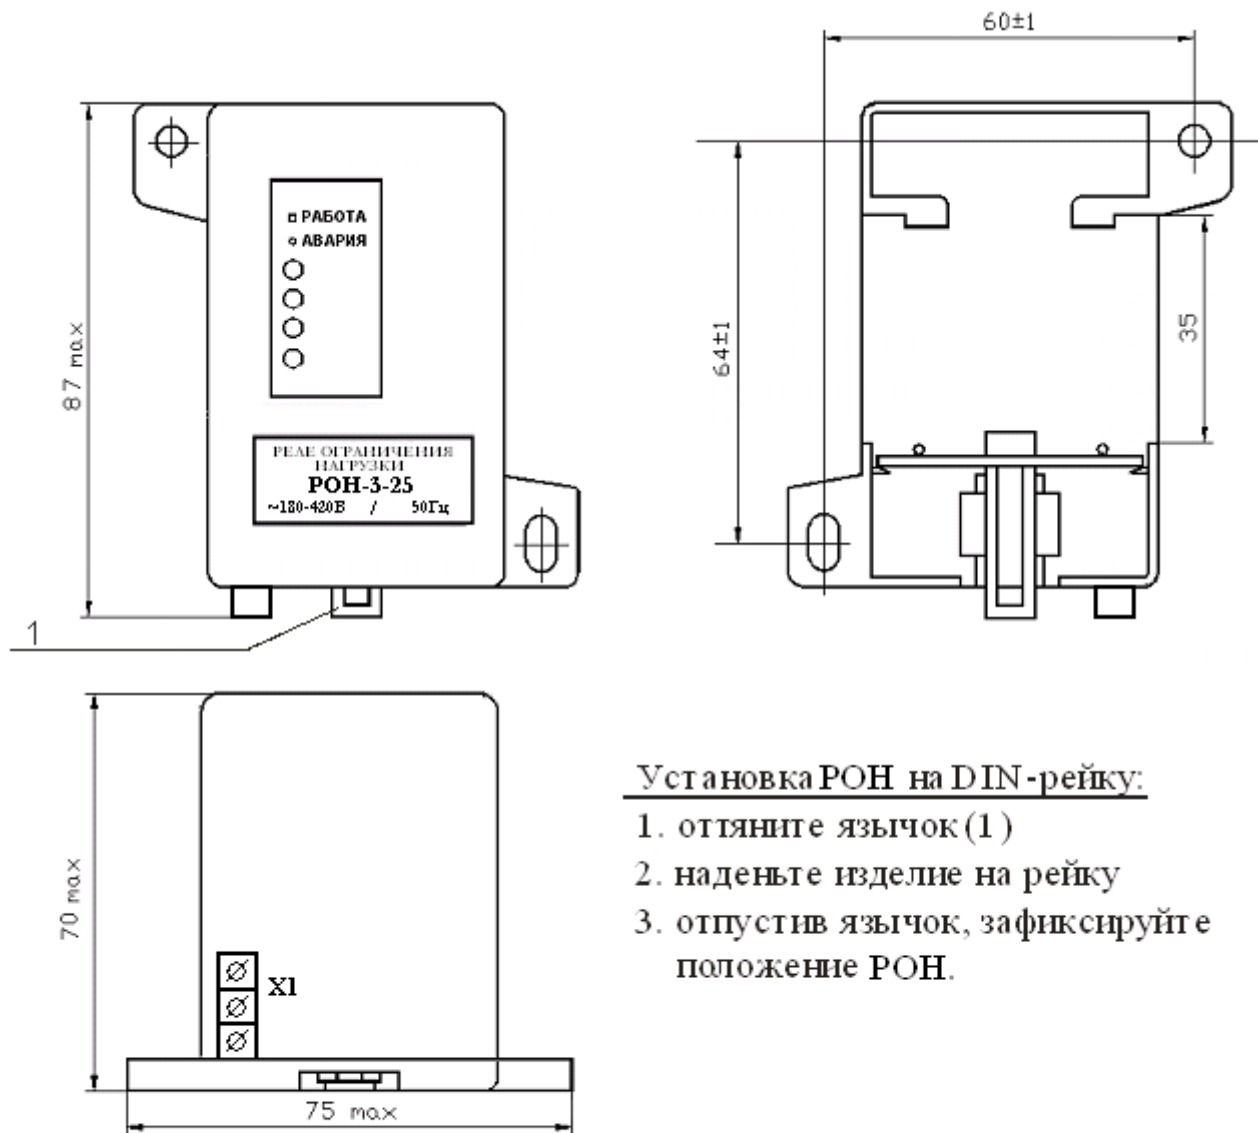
Габаритные и установочные размеры РОН без датчиков тока для крепления на винтовые соединения и на стандартную 35-мм DIN-рейку
